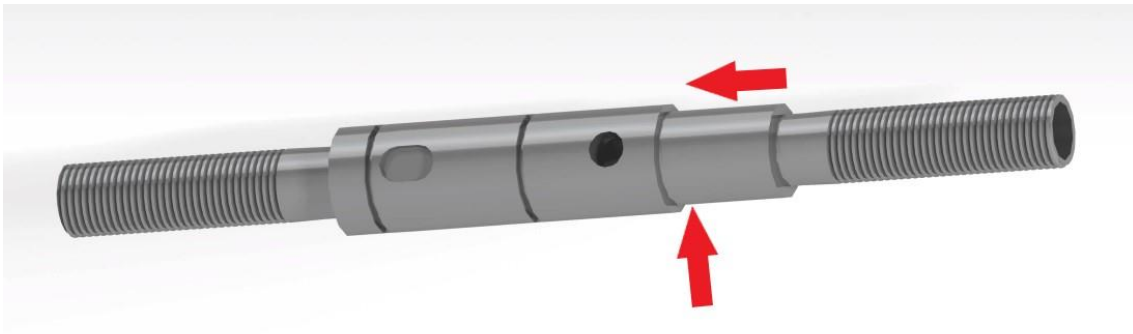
Vista en detalle del CILINDRADO_DESBASTE_2 del eje (Fuente: elaboración propia)
